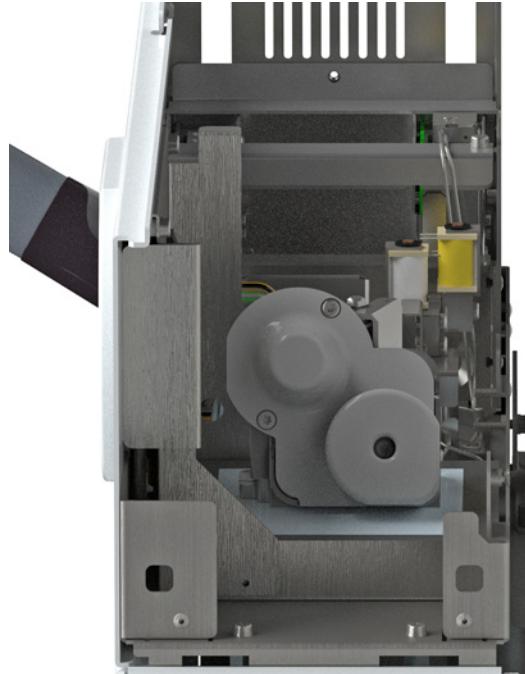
Pneumatikbaugruppe ohne Abdeckungen
